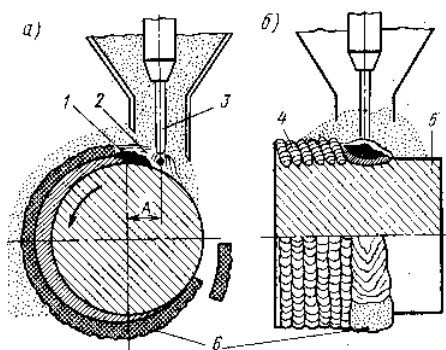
Схема наплавки под слоем флюса: а — поперечный разрез; б — продольный разрез; 1—ванна расплавленного металла; 2— расплавленный флюс; 3 - электродная проволока; 4 — наплавленный слой металла; 5 — деталь; 6 — шлаковая корка; А — смещение электродной проволоки с зенита
